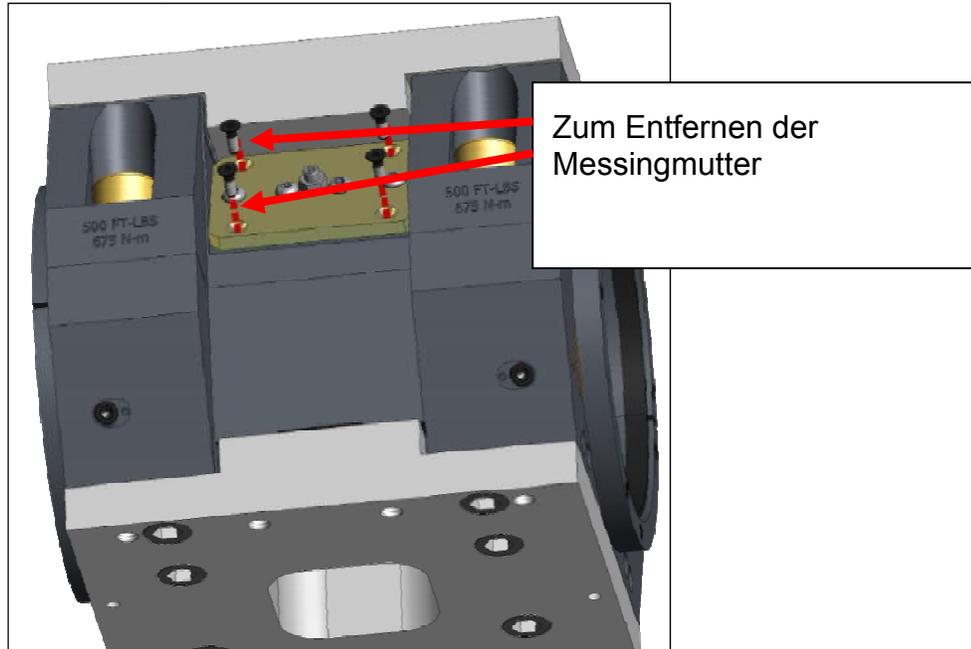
Schrauben zum Entfernen der Messingmutter
